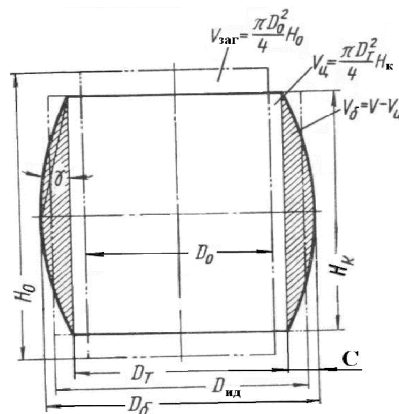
Форма и размеры осажённой цилиндрической заготовки [1]:
